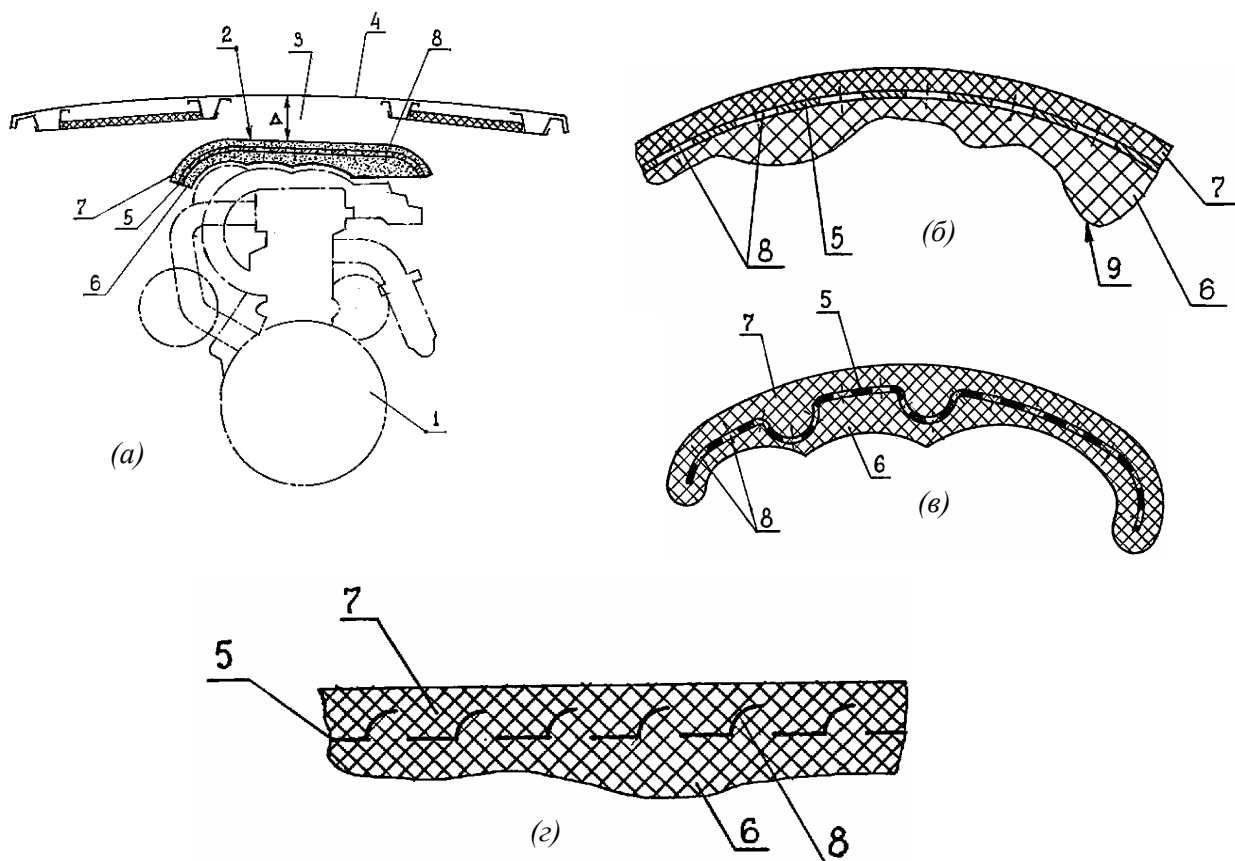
Схема установки ДВС в моторном отсеке автомобиля, верхняя часть корпуса ДВС охвачена шумоизолирующим кожухом типа объемного шумопоглощающего элемента корпуса ДВС (а), и варианты его конструктивного исполнения (б, в, г):
